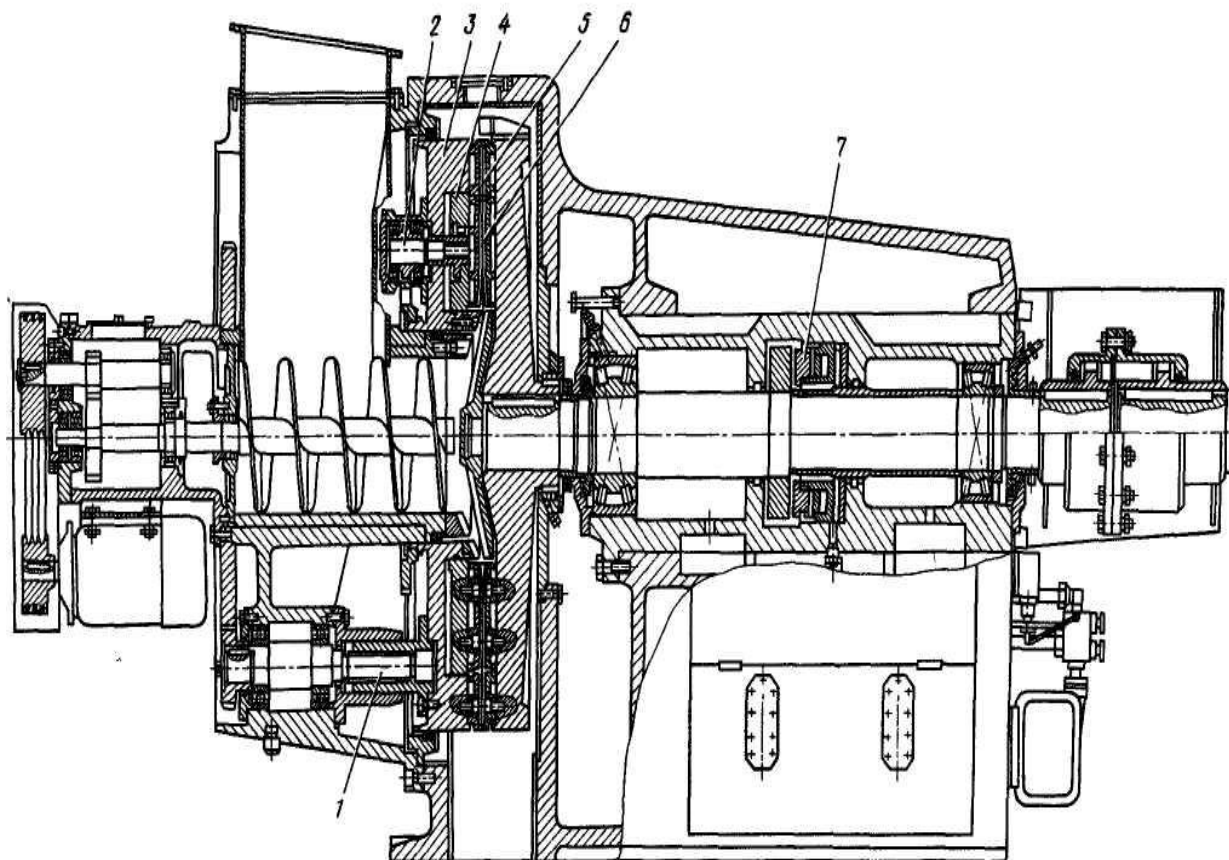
Однодисковая мельница с винтовой подачей массы: 1 - винтовые пары статора; 2 - винтовые пары статорного кольца; 3 - статор; 4 - статорное кольцо; 5 - гарнитура периферическая; 6 — гарнитура центральная; 7 — упорный подшипник скольжения
